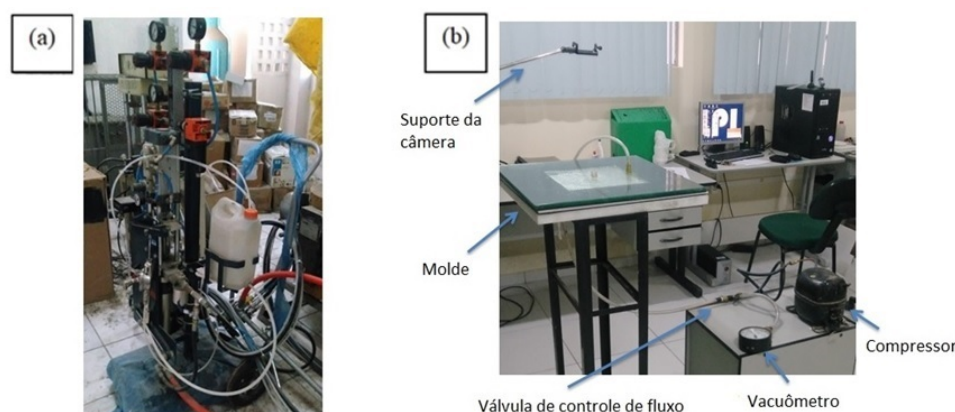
Sistemas utilizados para o processamento das placas. (a) máquina industrial para o método de RTM Light; (b) sistema adaptado para VARTM.
